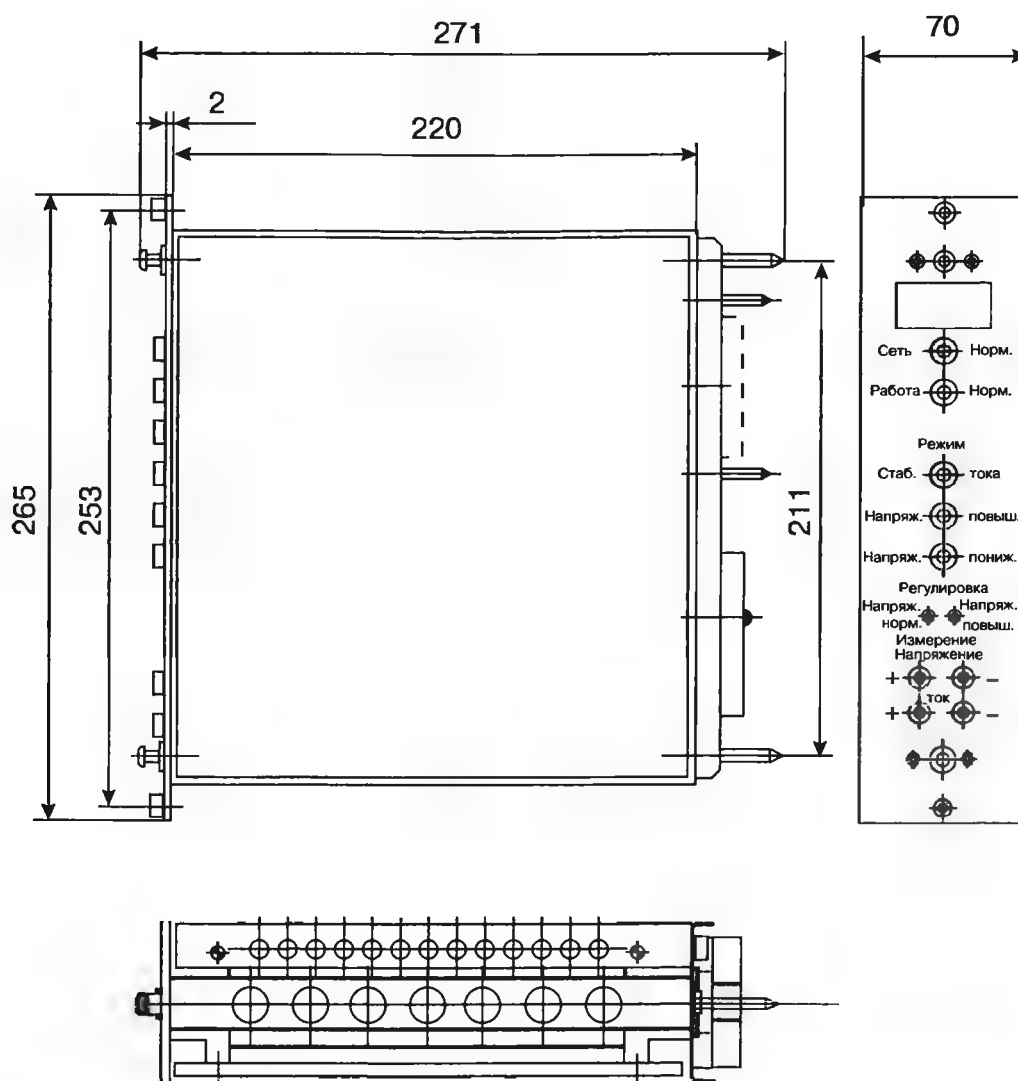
Общий вид блоков БПС-30В/10А-12(14) и их габаритные размеры
